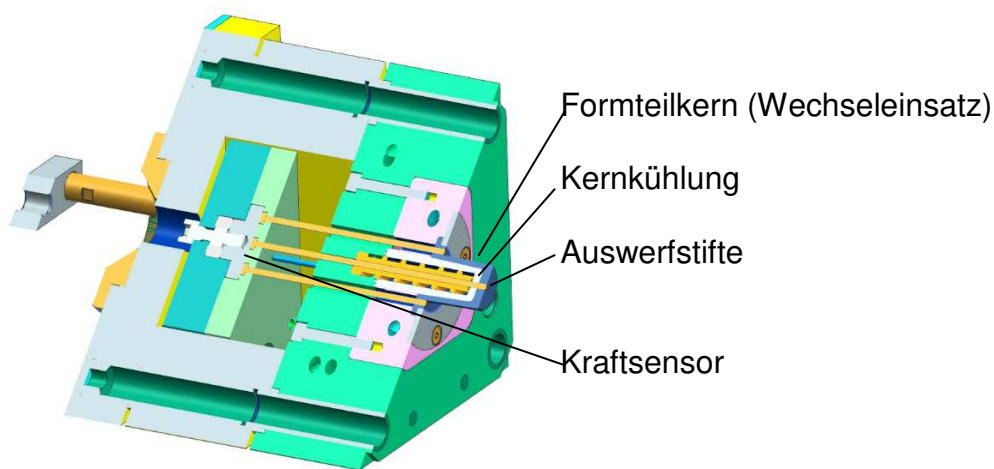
Schnitt durch Werkzeug - Entformungskraftmessung
